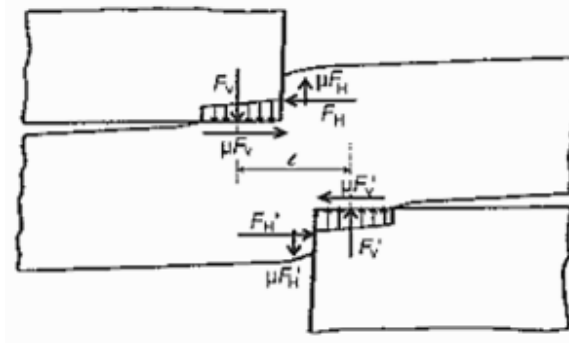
Distribución de fuerzas en la pieza de trabajo durante el corte por cizallamiento. Recuperado de [41].
